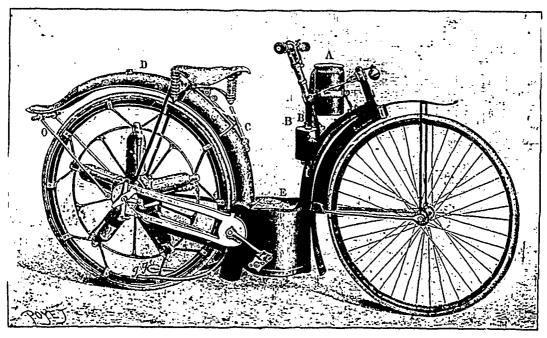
Le bicycle automobile Millet.—Vue d'ensemble du système.
